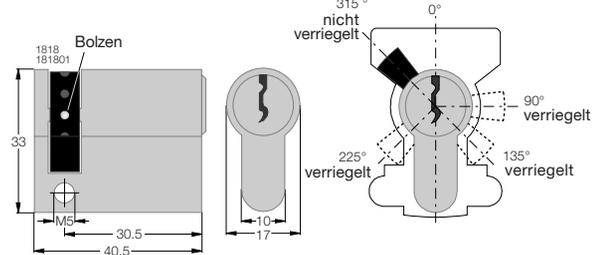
Schließzylinder [Best.-Nr. 1818, 1818 01]
